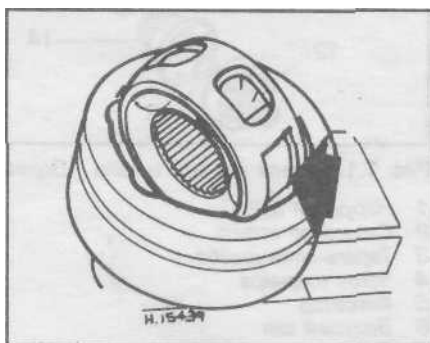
Извлечение сепаратора и ступицы из корпуса внешнего шарнира
